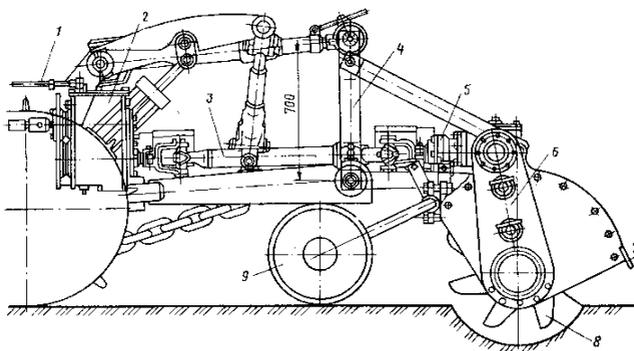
Фреза болотная навесная ФБН-2,0: 1, 3 – карданные валы; 2 – редуктор понижающий; 4 – рама с навеской; 5 – редуктор конический; 6 – редуктор цилиндрический; 7 – решетка грабельная; 8 – барабан фрезерный; 9 – опорные колеса
